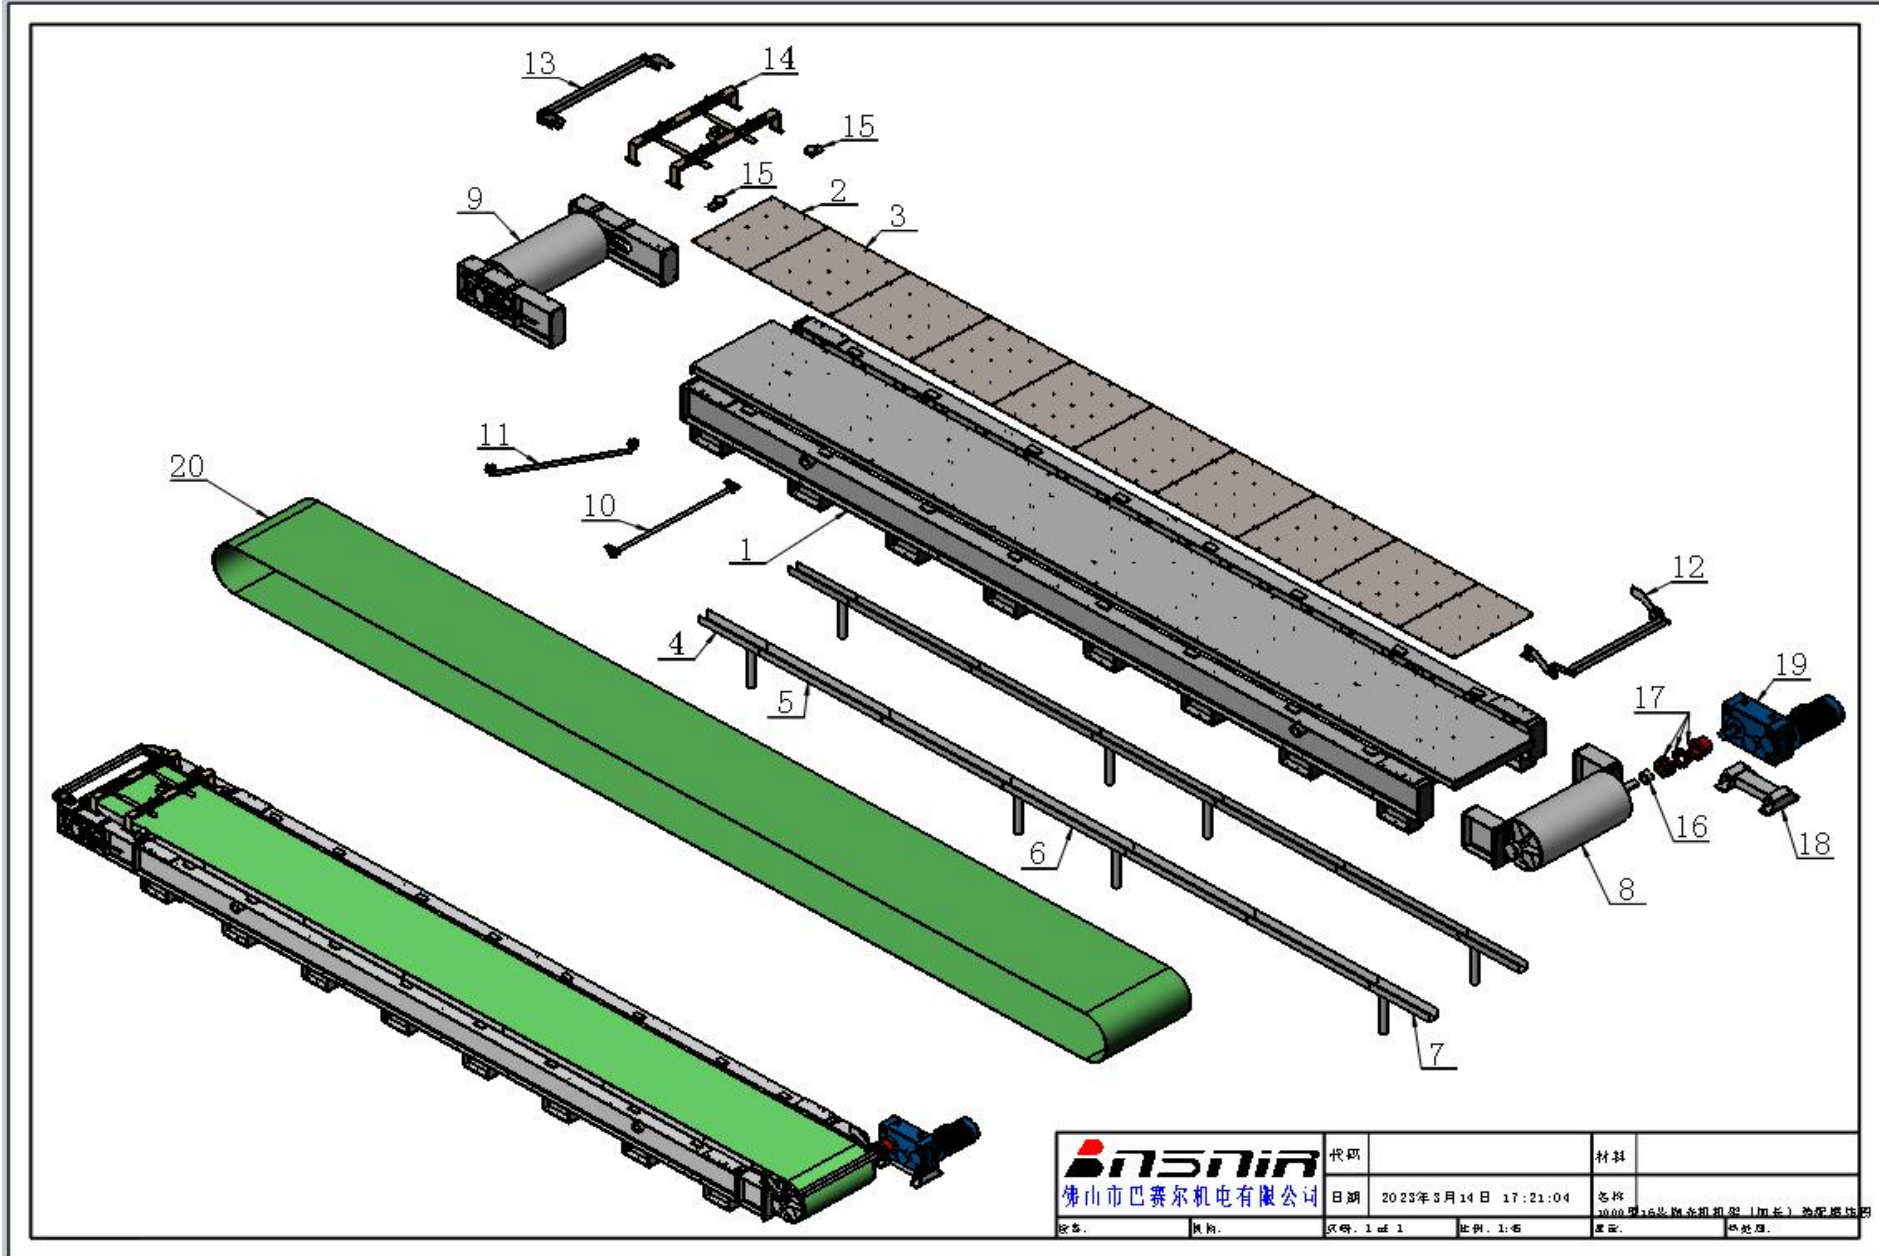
BP1000/16 抛光机——机架部分装配图 picture2 BP1000/16 polishing machine -- Rack part assembly drawing
